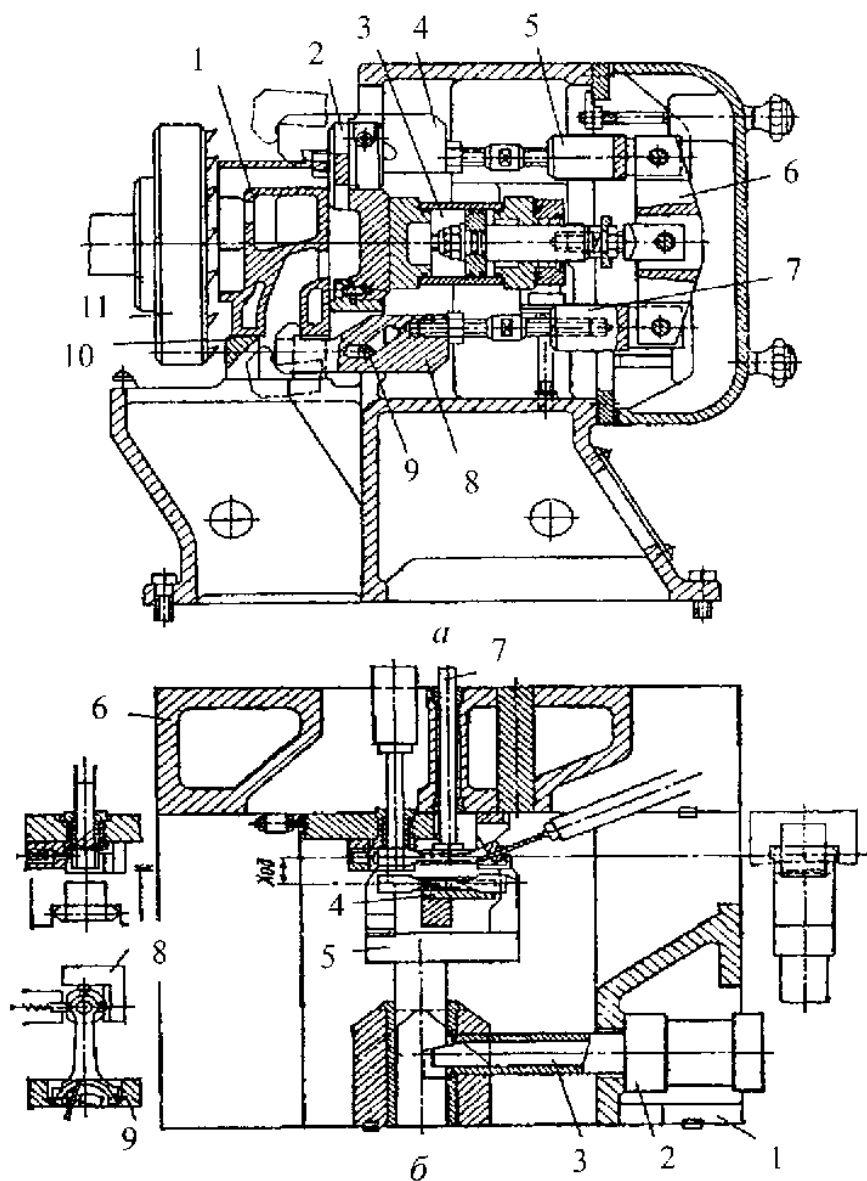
Стационарні пристрої: а) одноісний порталний типологічного типу з притисканням заготовки до низу; б) корпус; 2 – опорний платик; 3 – напрямна планка; 4 –
